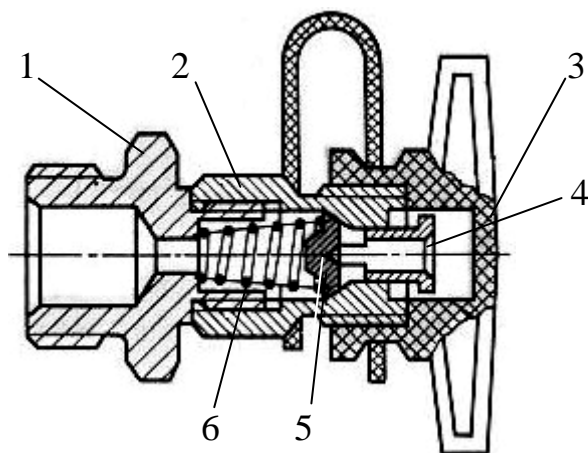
Клапан контрольного вывода: 1 – штуцер; 2 – корпус; 3 – защитный колпачок; 4 – толкатель; 5 – клапан; 6 – пружина
